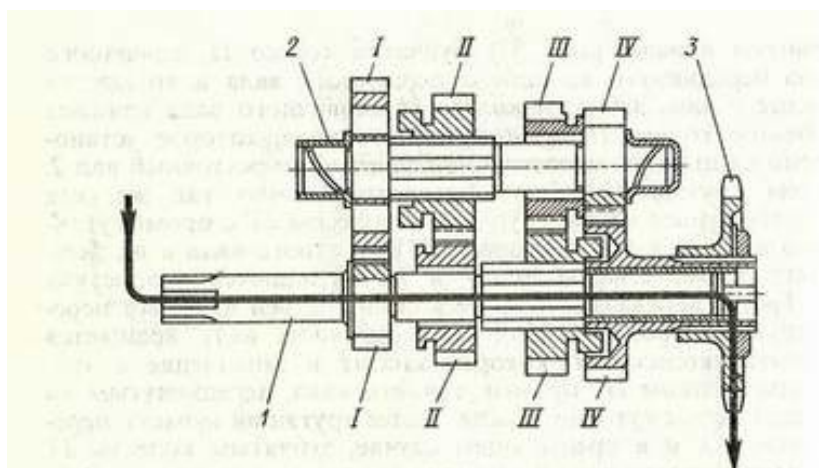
Положение зубчатых колес при включении четвертой передачи
